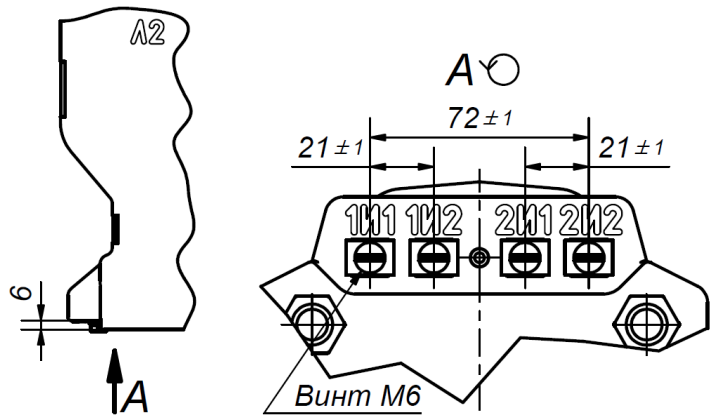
Габаритный чертеж трансформатора тока с нижним расположением контактов вторичных обмоток ТОЛУ-10-1.2Н. Остальное см. на рис. 1.
